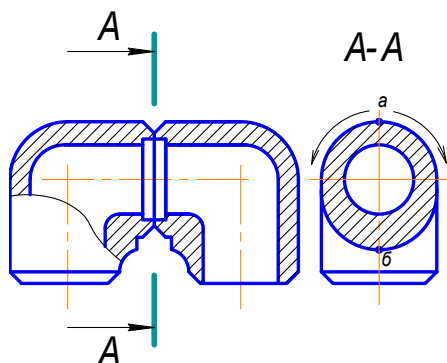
Сварное изделие с переменной толщиной стенки
